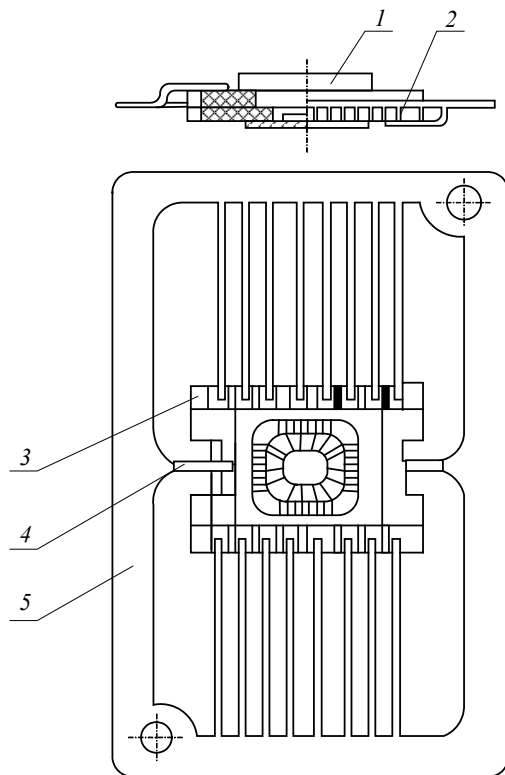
Плоский металлокерамический корпус с планарными выводами:
